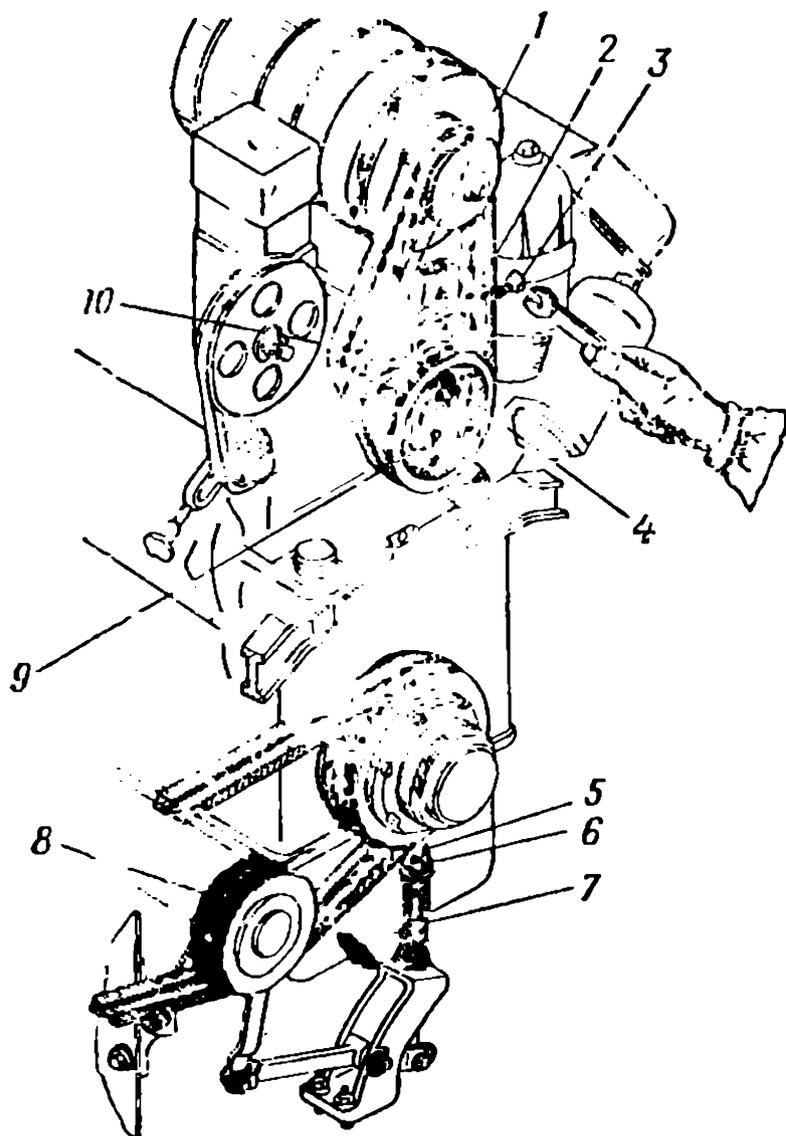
Натяжение ремней генератора и редуктора вентилятора:
